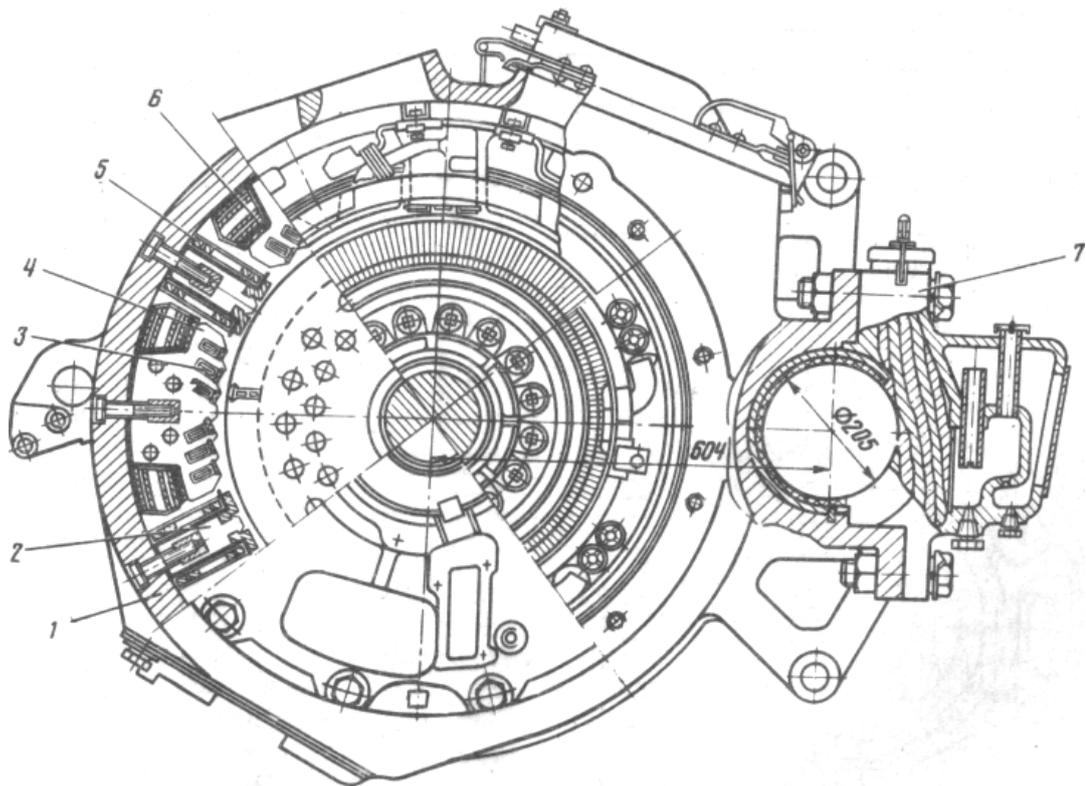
Поперечный разрез тягового двигателя НБ-418К6:
